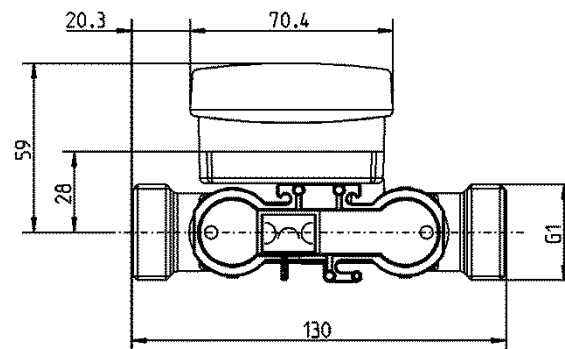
Übersicht Maße Baulänge 130 mm (Gewinde)
